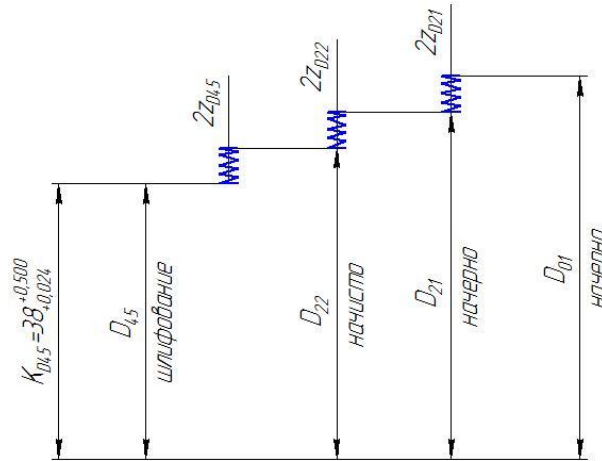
Размерная цепь для шейки $\varnothing 38$
